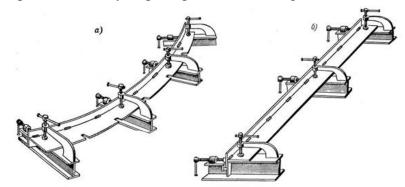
Простейшие кондукторы на базе ручных винтовых прижимов: a - для сборки криволинейных балок, b - dля сборки прямых балок.
